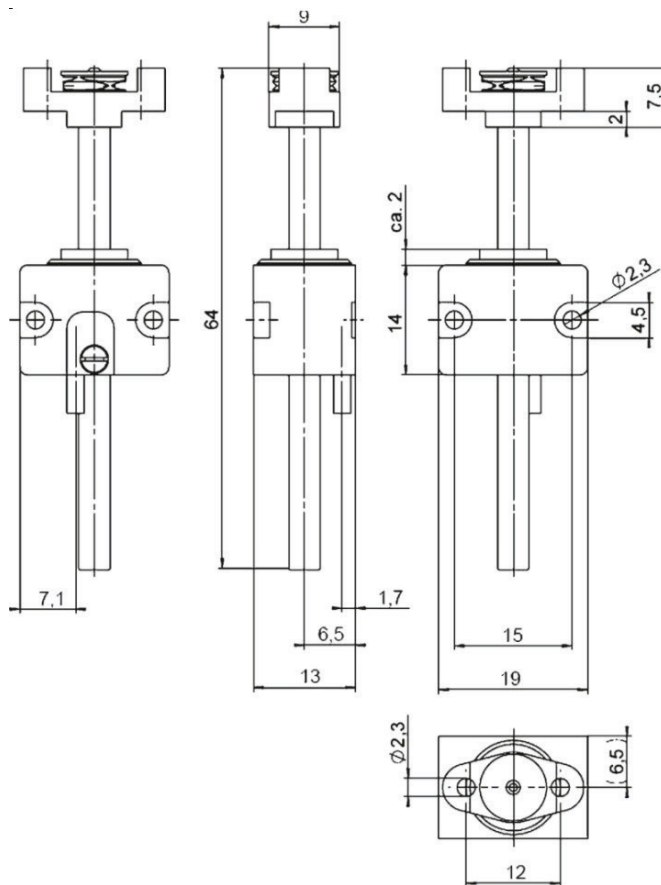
Габаритный чертёж N-422.50. Размеры указаны в мм.
